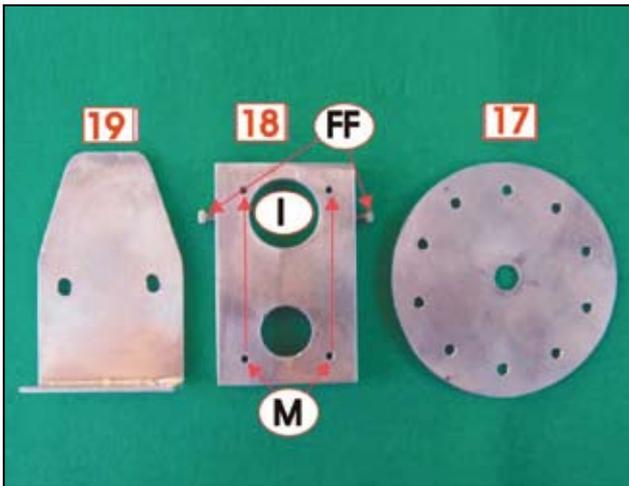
Particolari per il fissaggio del motore e disco encoder.
